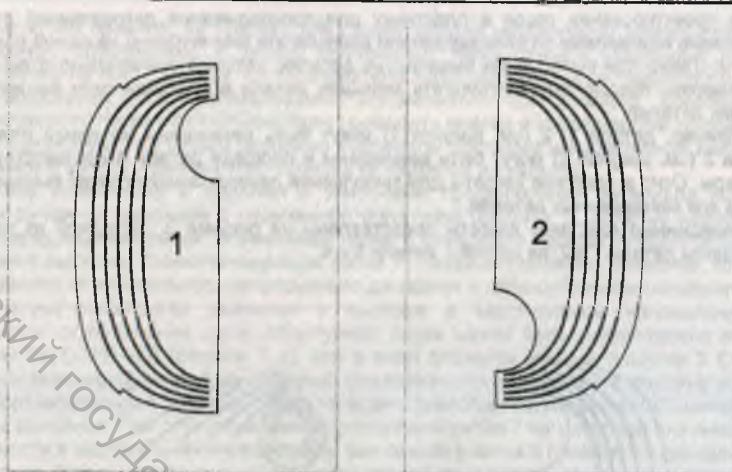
Детали правого и левого голенищ сапог с декоративными строчками
